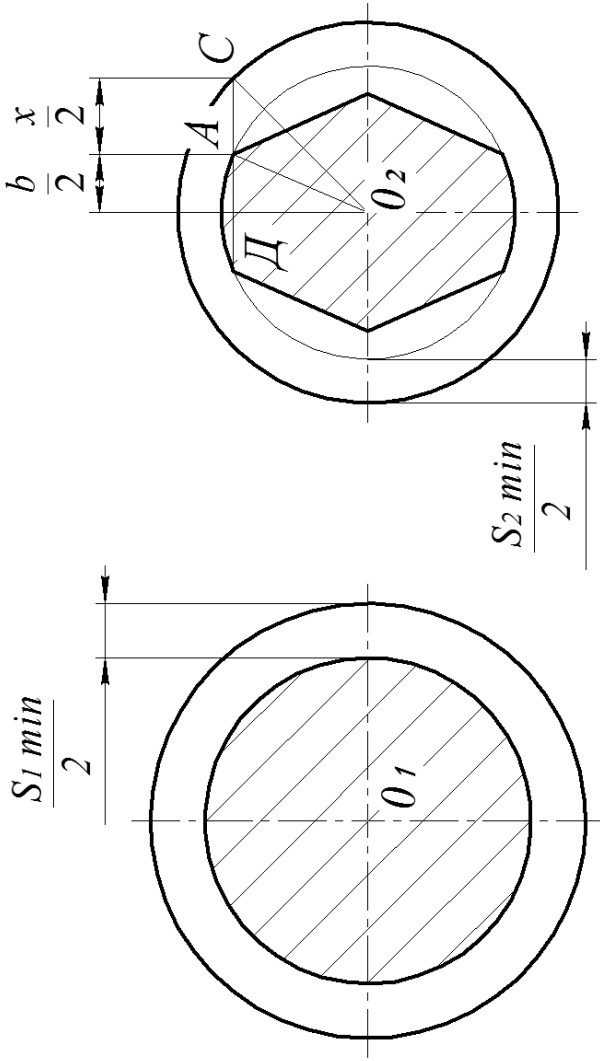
Розрахункова схема для визначення ширини стрічки зрізаного пальця
